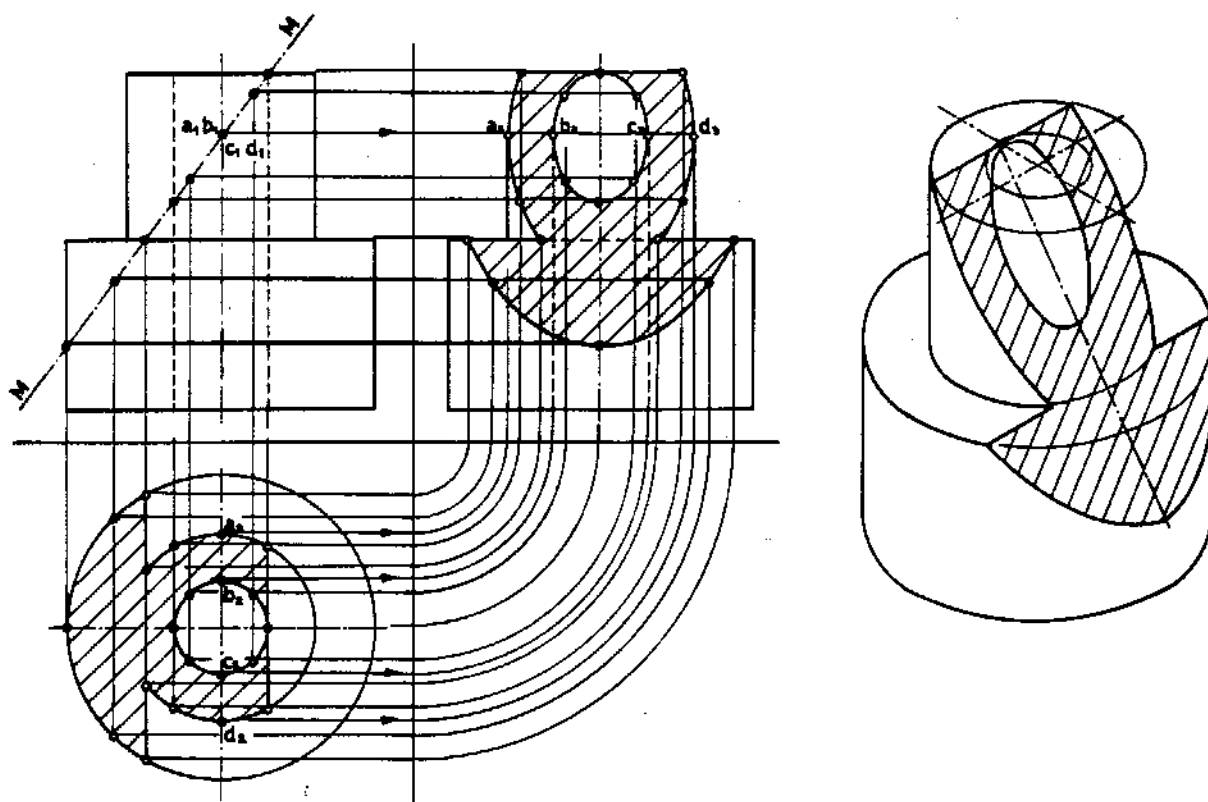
Sezione di un solido a doppio corpo cilindrico mediante un piano di traccia MM perpendicolare al P.V. e inclinato rispetto al P.O.
